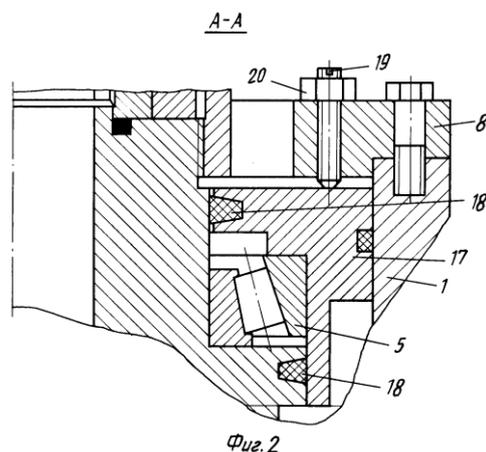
Усовершенствуемый узел в конструкции вертлюга
